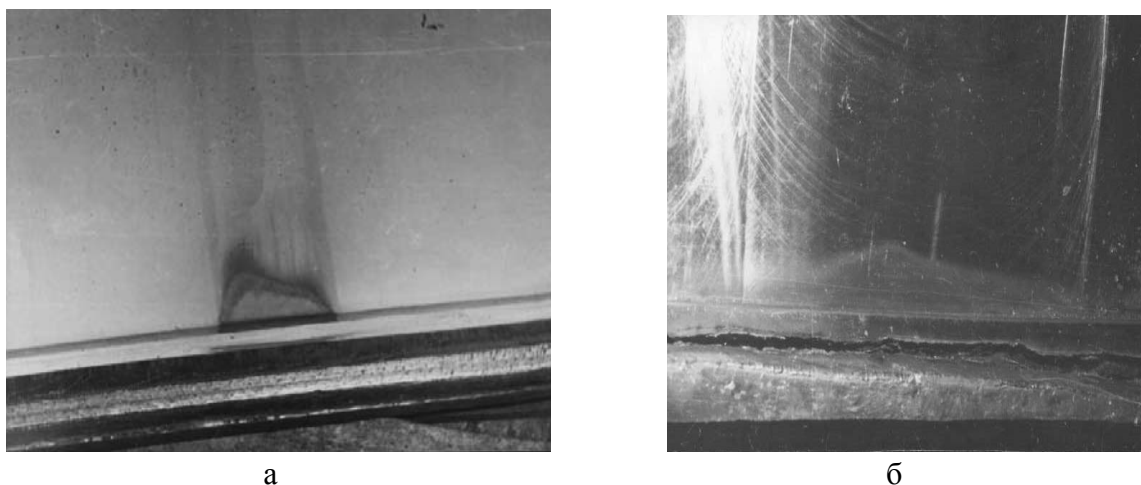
Окисленные зоны после ручной сварки (а) и после сварки на автоматической линии (б)
